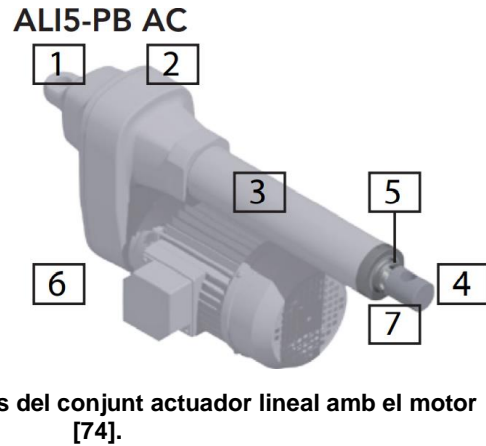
Aspecte i parts del conjunt actuador lineal amb el motor [74].
